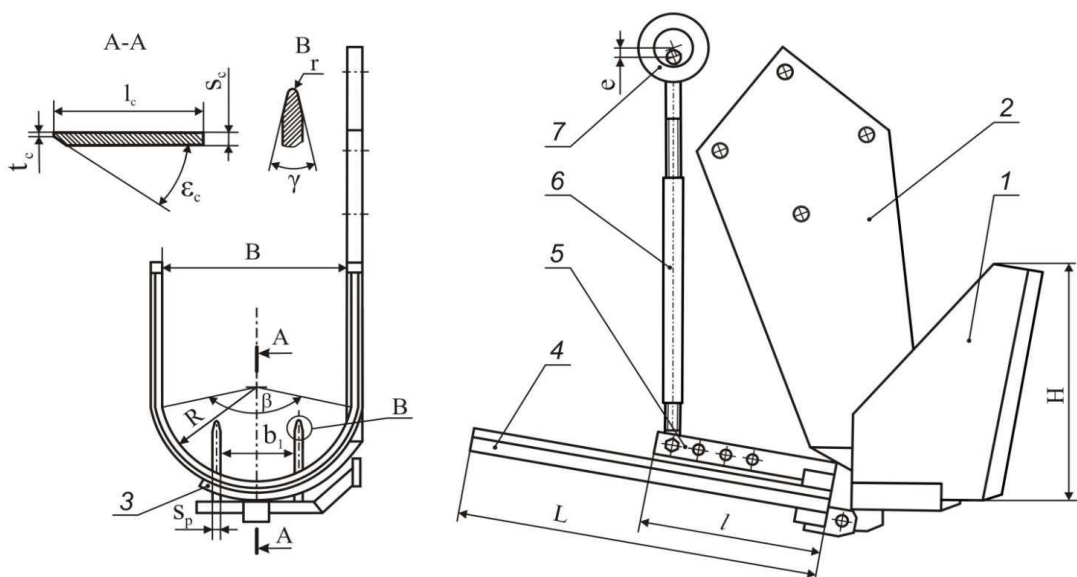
Геометричні характеристики елементів конструкції робочої частини викопувального плуга: 1 – робоча скоба для викопування; 2 – опорна стійка; 3 – башмак-опора; 4 – елемент для розпушування ґрунту; 5 – важільний механізм; 6 – тяга з ексцентриковим приводом; 7 – ексцентриковий вузол.
